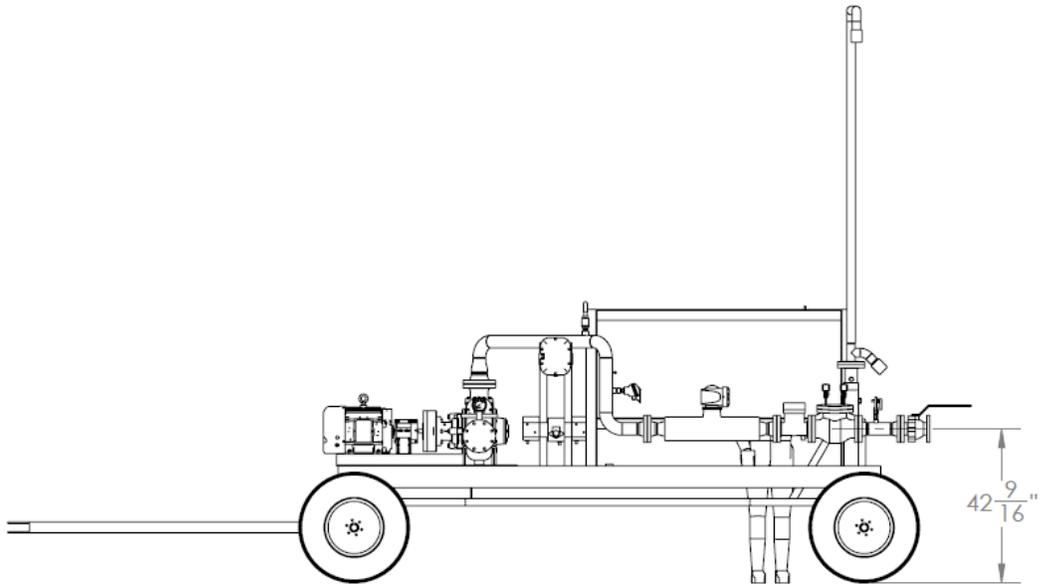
Dimensiones del Transloader – Vista frontal posterior
